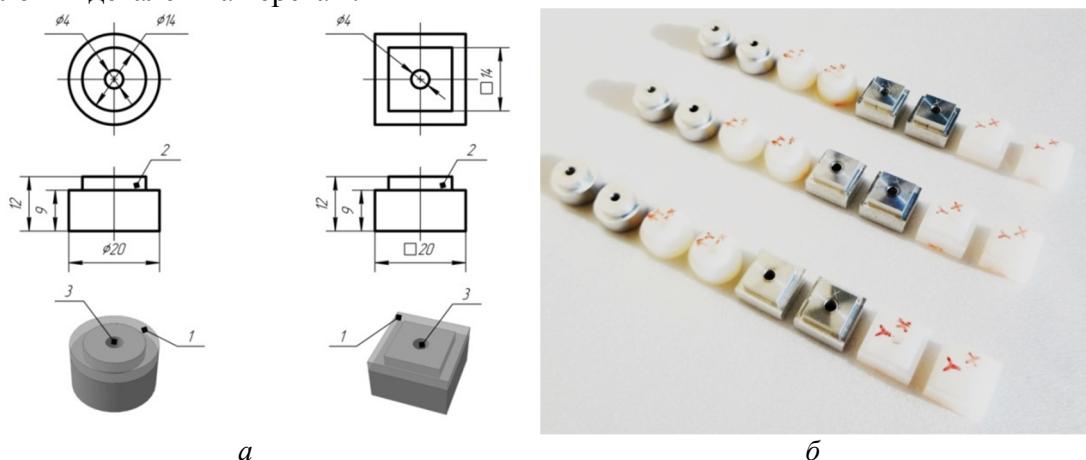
Зразки деталей, що оброблялися: а – креслення; б – оброблені зразки
